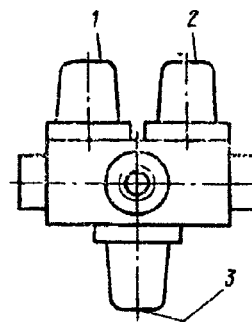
Расположение регулировочных винтов тройного защитного клапана:
